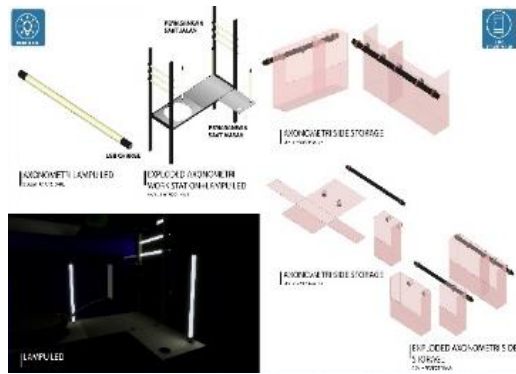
Detail Axonometri Komponen dan Detail Sambungan Area Masak, Area Persiapan, Media Penjualan, Area Penyimpanan, dan Etalase
